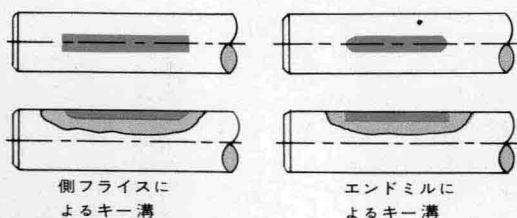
キーの型(P. H. Black and O. E. Adams, Jr., Machine Design, 1968)
